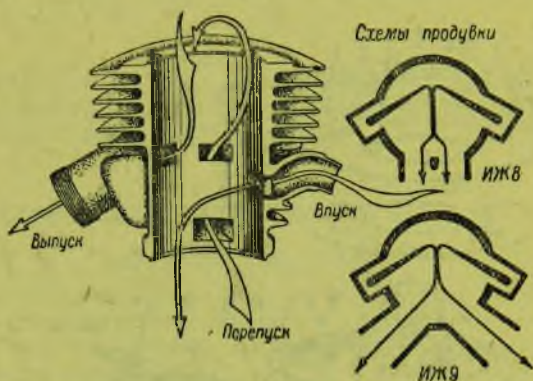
Цилиндр двигателя ИЖ-9 и схемы продувки ИЖ-8 и ИЖ-9
